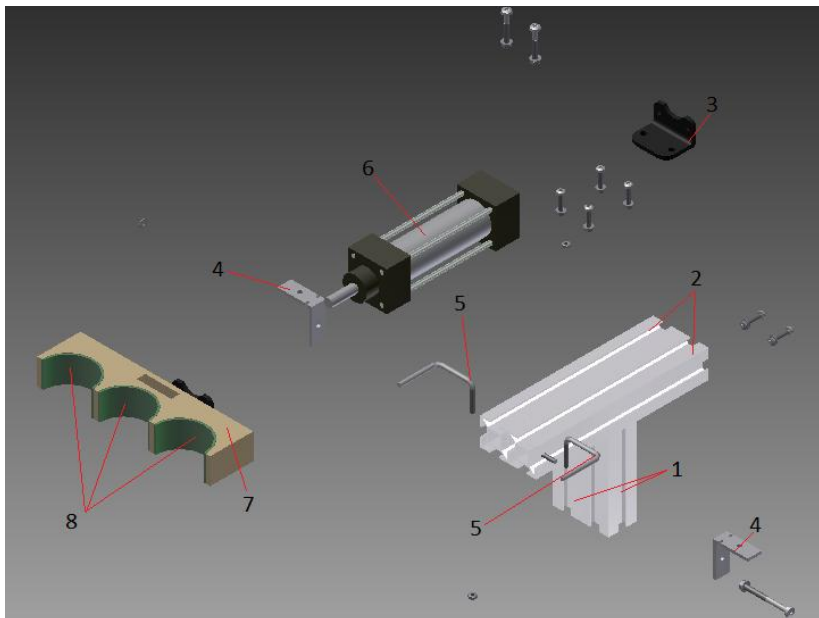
4 Ensamble del soporte del cilindro horizontal
